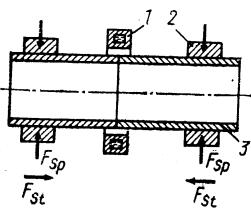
Стыковая сварка труб с кольцевым индуктором под действием сжимающего усилия:
